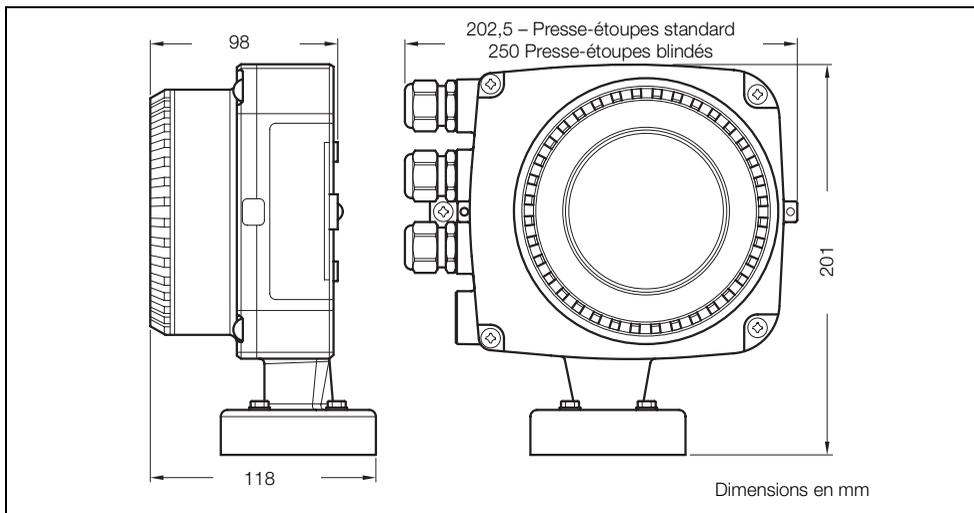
Dimensions du transmetteur intégré (Presse-étoupes standard montés)
